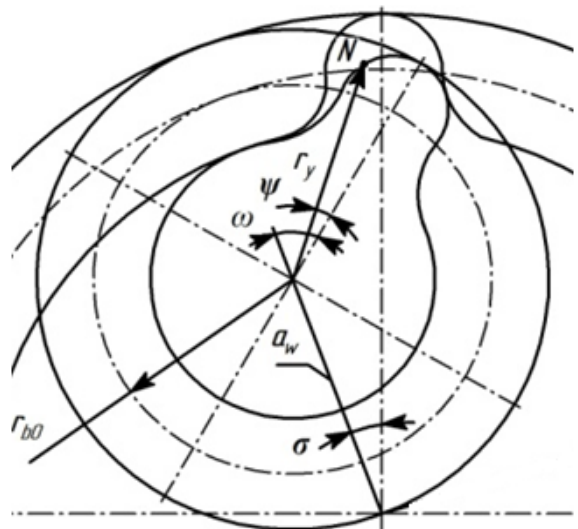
Схема определения положения зуба долбяка относительно зубчатого колеса при комплексном анализе процесса формообразования.
